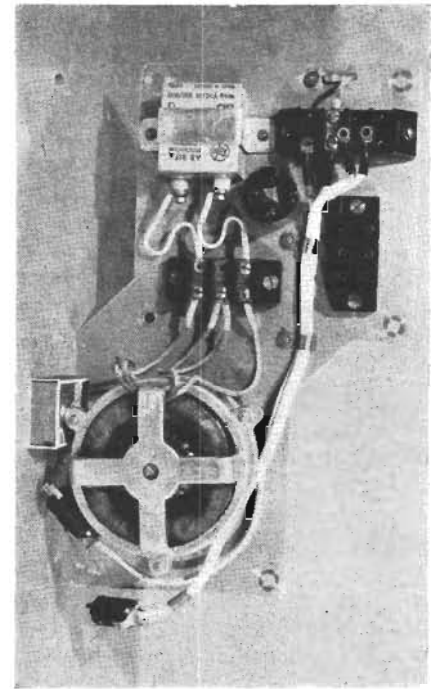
Montageplatta C med sin drivmotor, motor M_3 , m.m.
